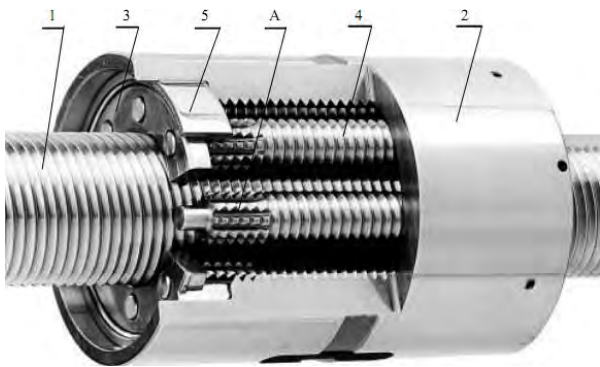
ПРВМ с зазором между резьбовыми деталями
